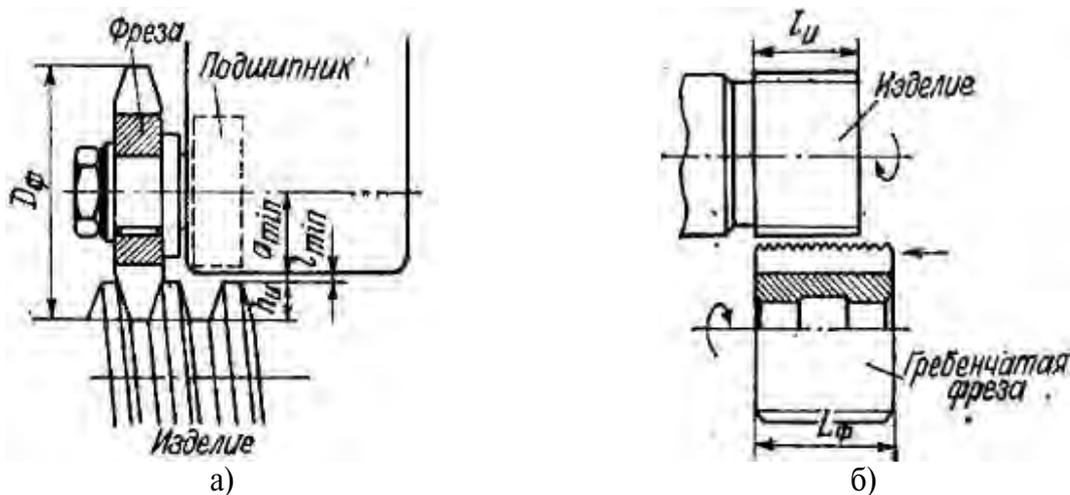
Схемы фрезерования резьбы гребенчатыми резьбовыми фрезами:
